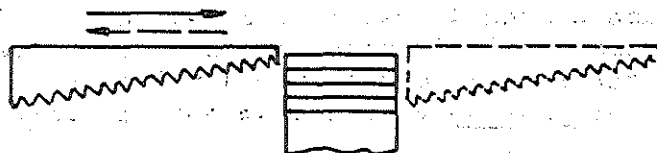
Brochagem com máquina horizontal. Peça fixa e ferramenta em movimento.
